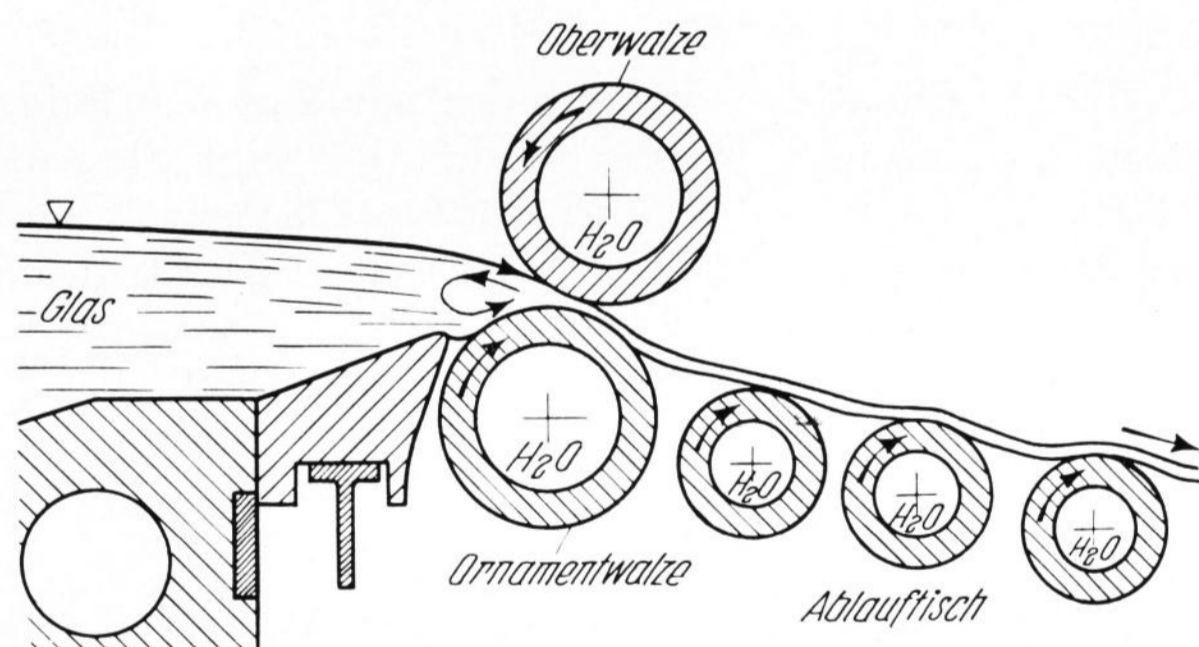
Strömung vor dem Walzenspalt beim Walzen von Ornamentglas (Versuch 6).
